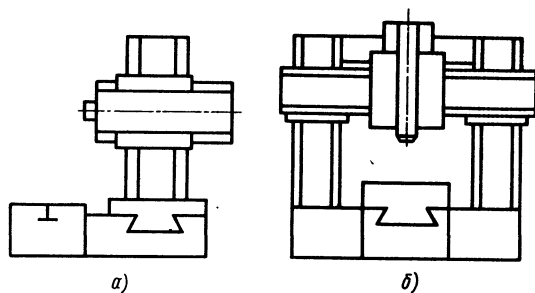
Варианты компоновок станка с расположением шпинделя: а — горизонтальным; б — вертикальным
